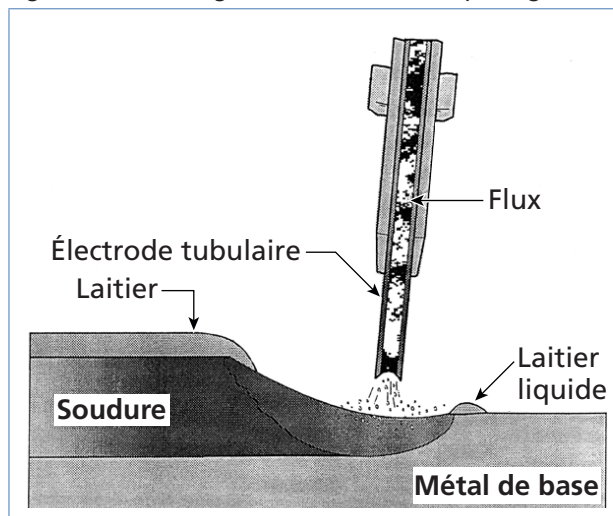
Soudage avec fil fourré et gaz de protection
